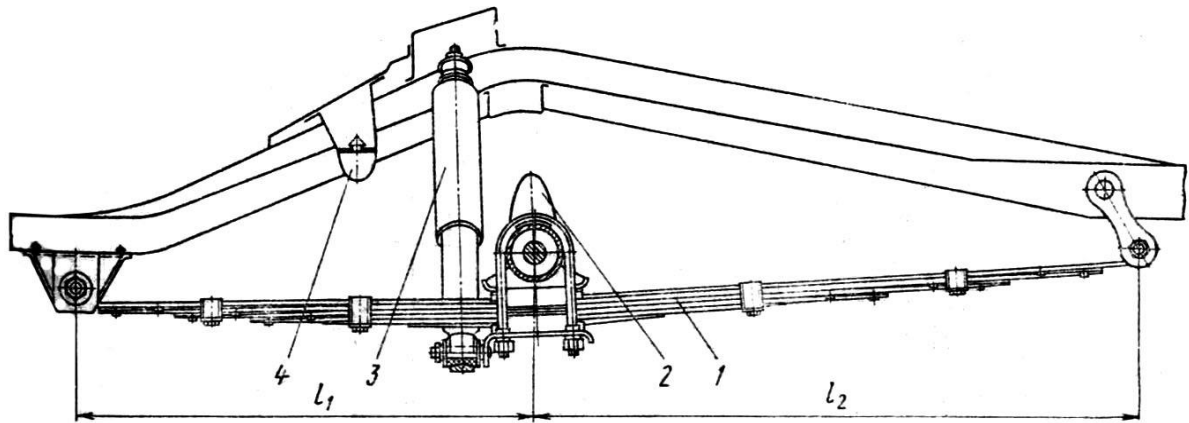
Задня підвіска легкового автомобіля з несиметричною листовою ресорою: 1 – ресора; 2 – буфер стиску; 3 – амортизатор; 4 – додатковий буфер
